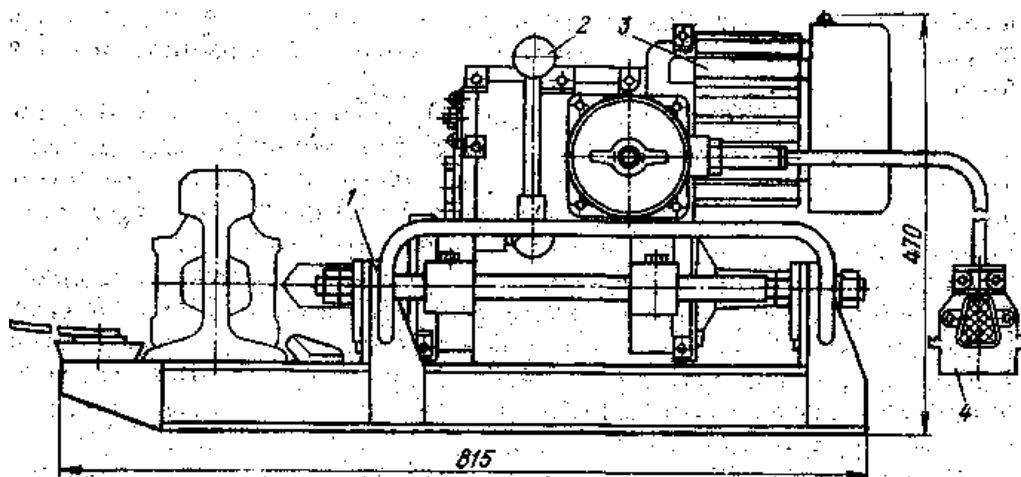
Рельсосверлильный станок РСМ-1:
